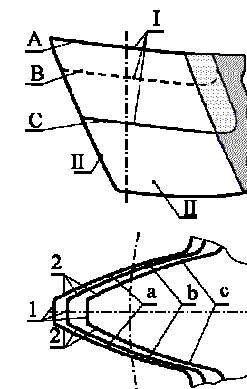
Зуб и режущие кромки лезвийных инструментов:
